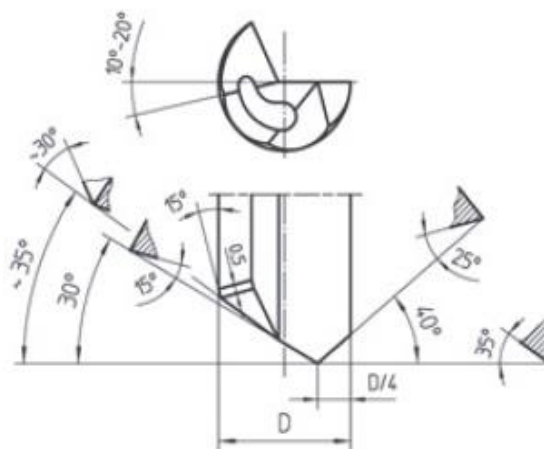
Стандартная заточка для диапазона сверления 1,850 – 4,000 мм ружейного сверла Botek
